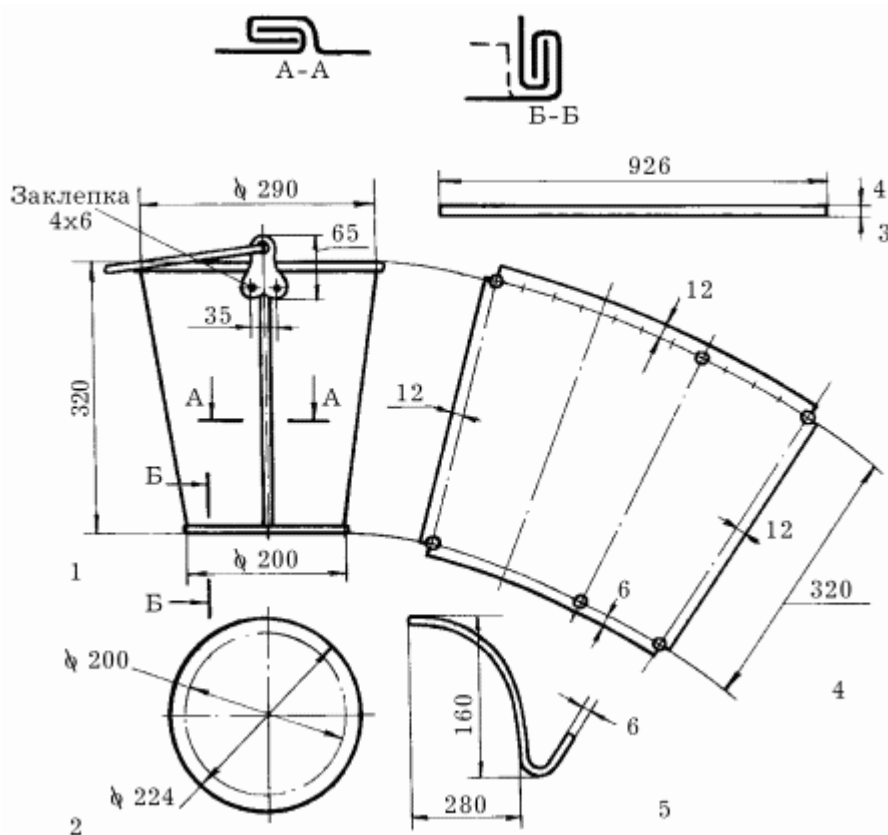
Цилиндрическое ведро: 1 – общий вид ведра; 2 – заготовка днища ведра; 3 – проволочный ободок в развернутом виде; 4 – половина обечайки; 5 – дужка ведра.
